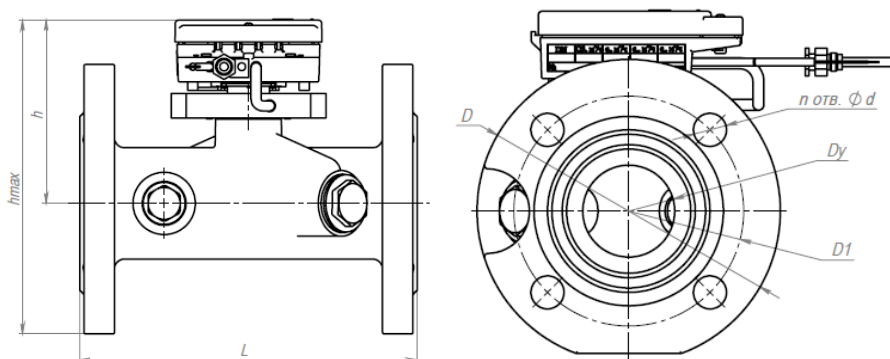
Габаритные и присоединительные размеры для расходомеров со степенью защиты оболочки IP54
